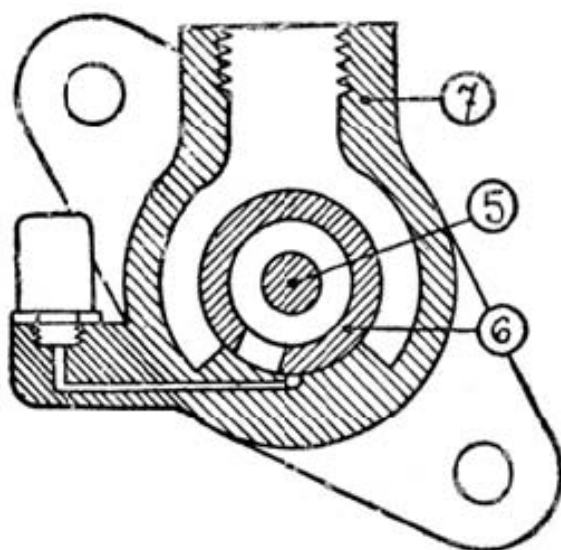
Corte transversal del deshollinador Dalmar por la entrada de vapor, mostrando la parte ciega que sella la salida durante una parte de la rotación.
